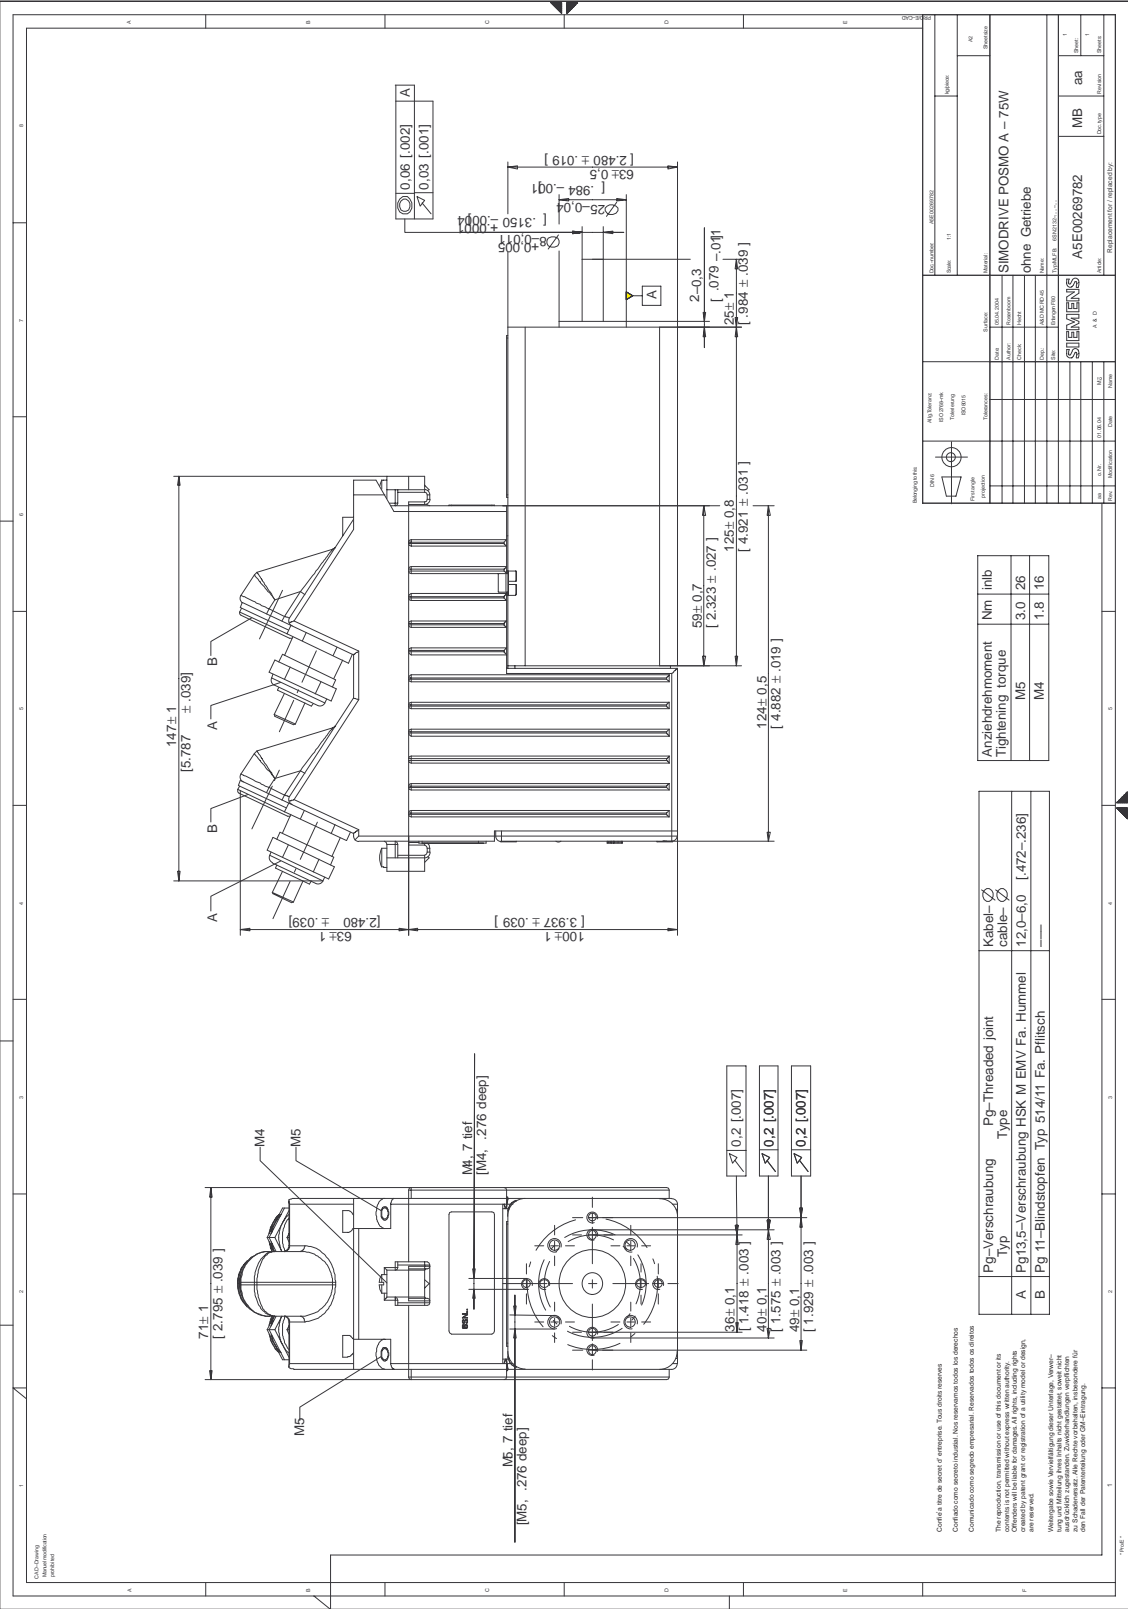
Maßblatt: SIMODRIVE POSMO A – 75 W ohne Getriebe
